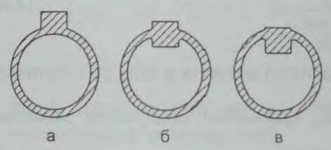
Схемы расположения термического узла на отливке цилиндрического типа
